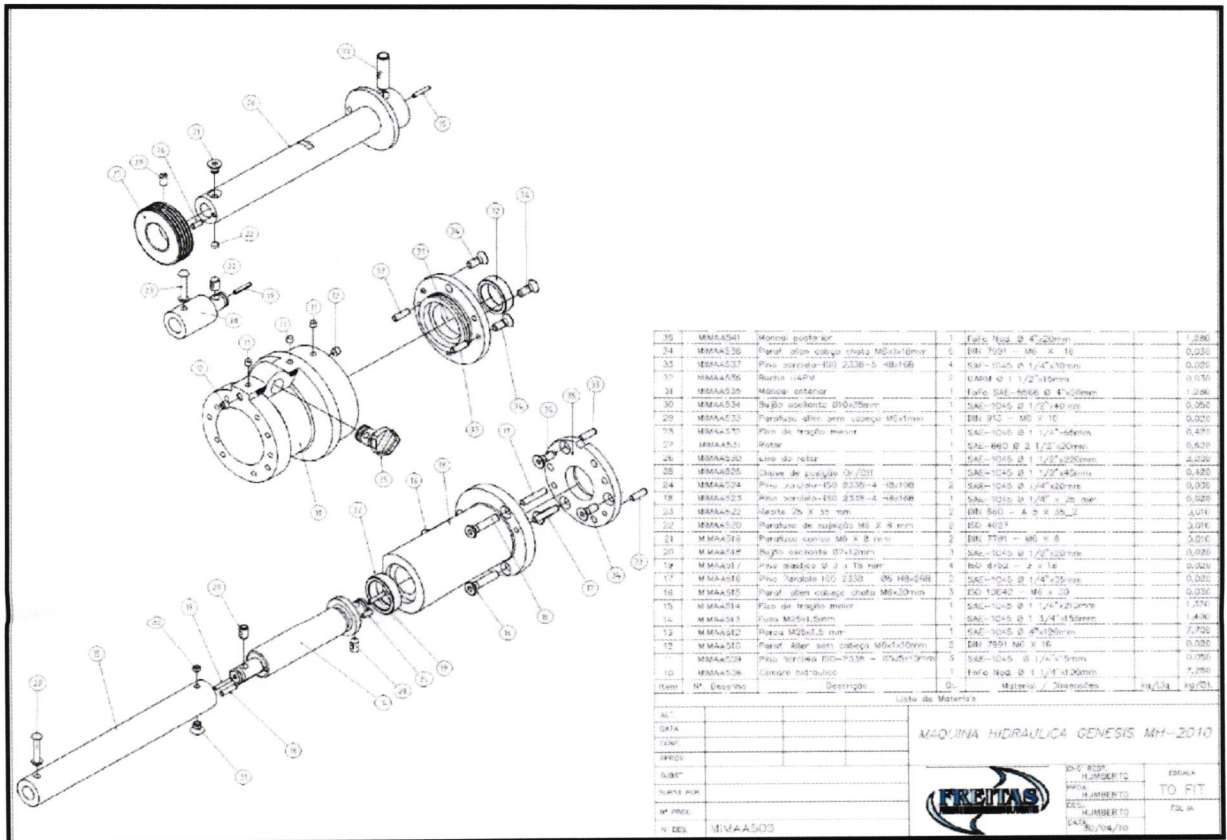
Desenho da Vista explodida da máquina hidromecânica
